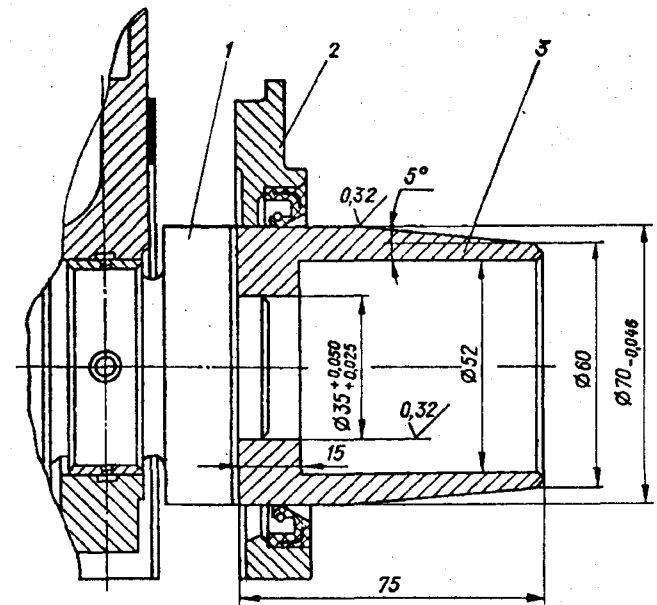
Установка держателя манжеты на фланец коленчатого вала: 1 – коленчатый вал; 2 – держатель манжеты; 3 – оправка
